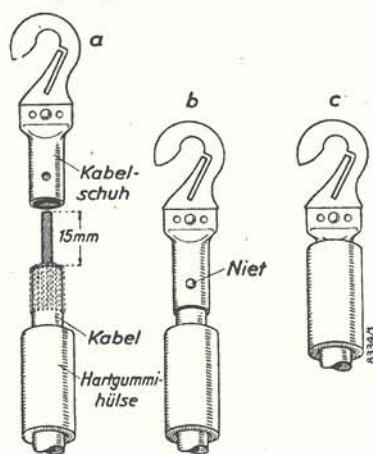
Befestigen des Rajah-Kabelschuhs am Kabel
